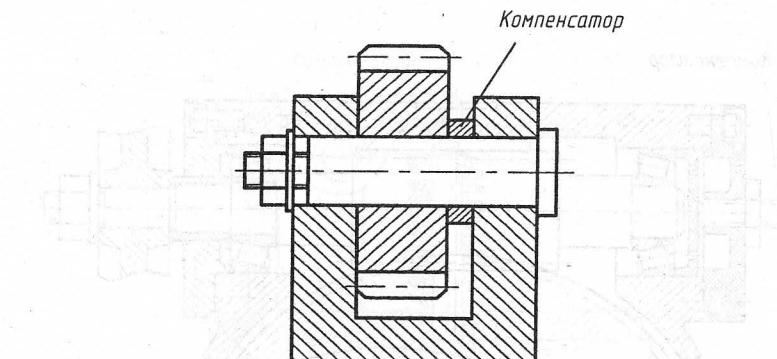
Способ обеспечения осевого зазора между торцом зубчатого колеса и стенкой корпуса
